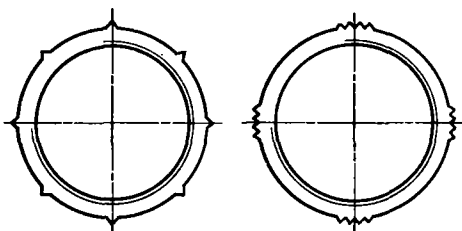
Кольцевые гайки с треугольными шлицами и выступами
